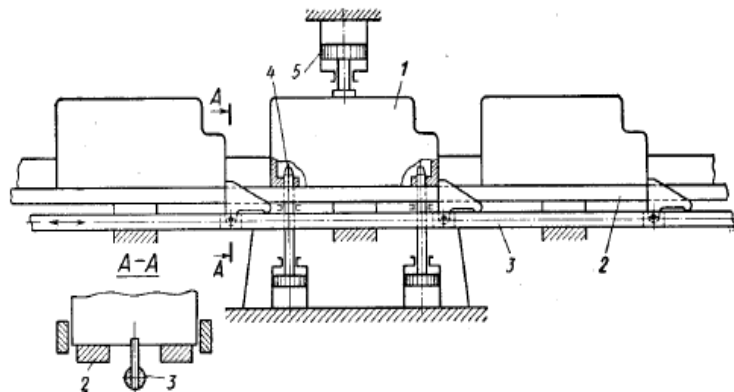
Схема пристосування для переміщення і установки корпусних заготовок на автоматичній лінії
